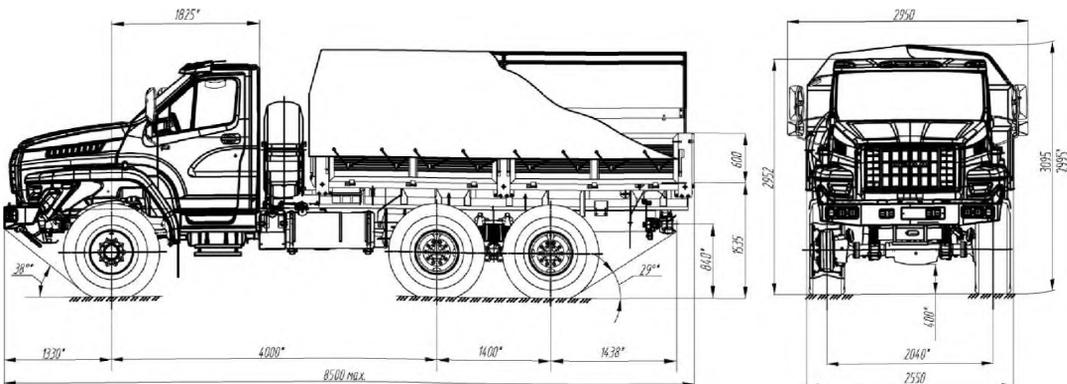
Габаритные размеры автомобиля Урал-4320-5111-73/75
